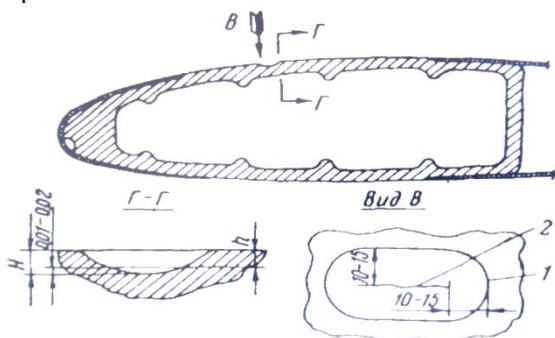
Вскрытая риска или царапина на поверхности металлической части лонжерона несущего винта вертолёта Ми-8 [8]
